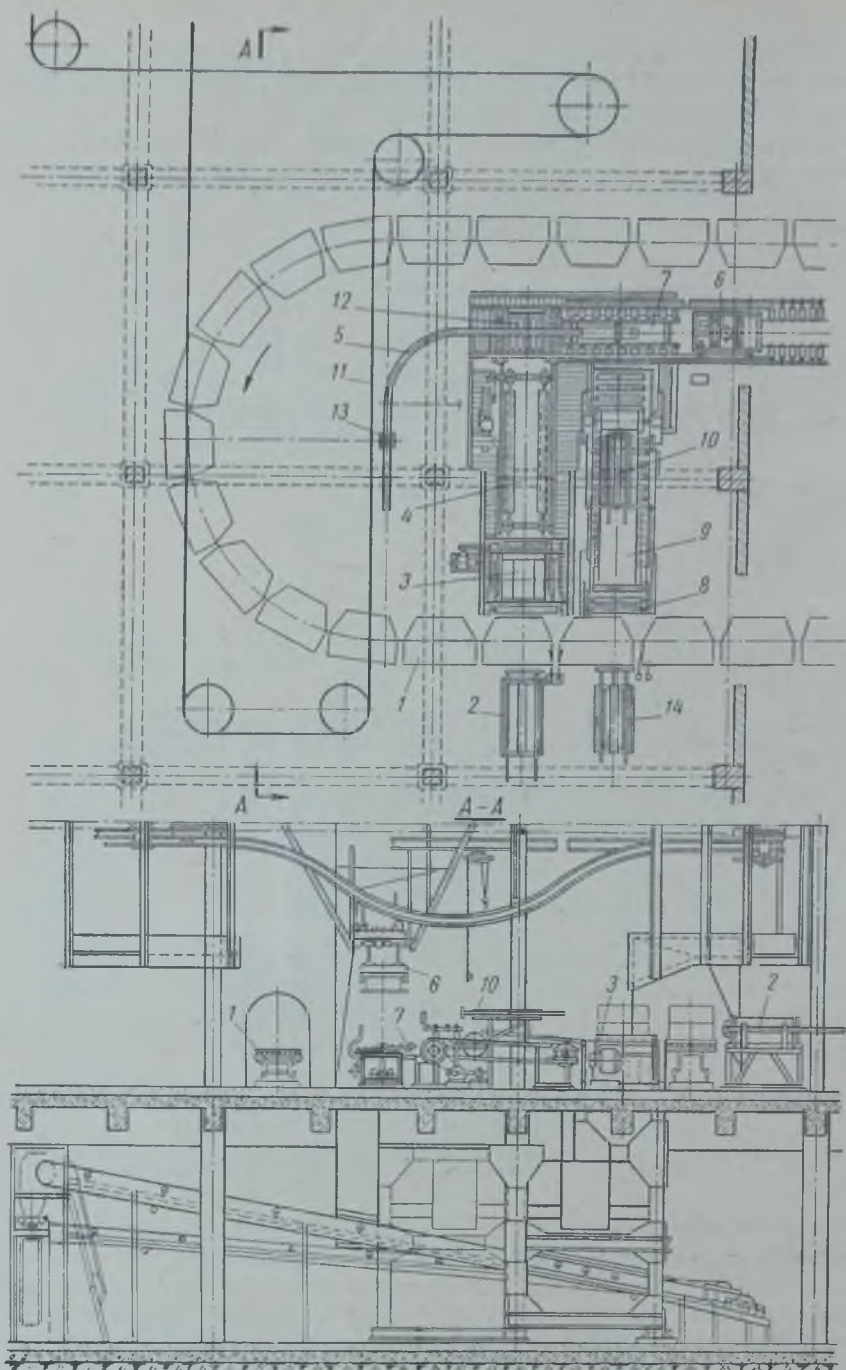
Схема полуавтоматической выливной установки конструкции ЗИЛ для отливок блока цилиндров
